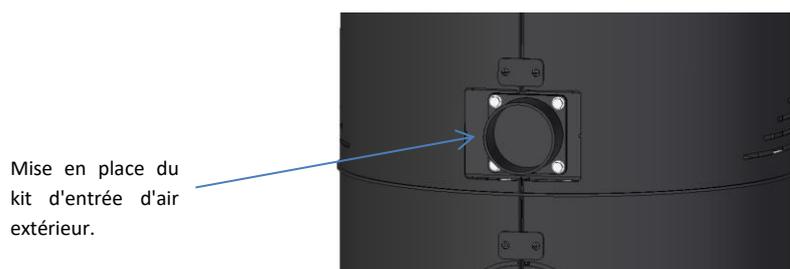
Vue arrière de l'équipement, placement du kit d'entrée d'air extérieur
